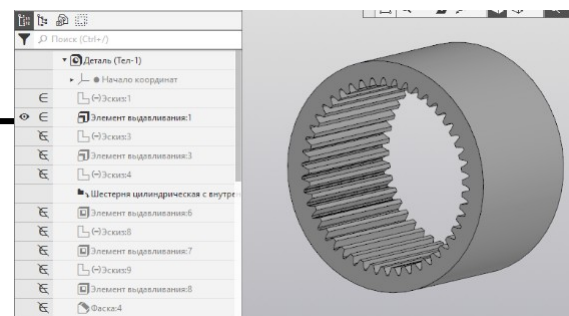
Добавляю зубчатый венец на деталь согласно данным на чертеже
